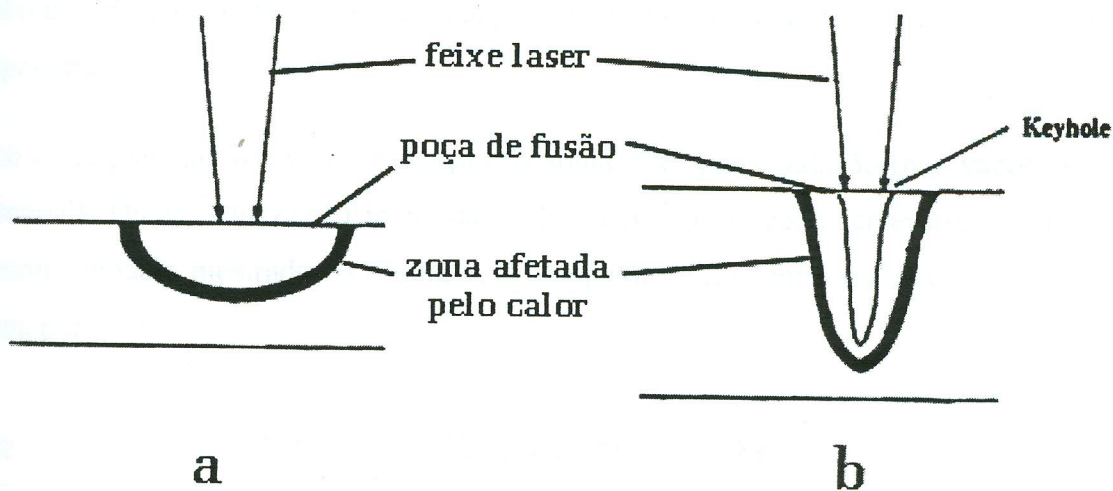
Desenho esquemático das técnicas de soldagem a laser: (a) condução, (b) penetração.
